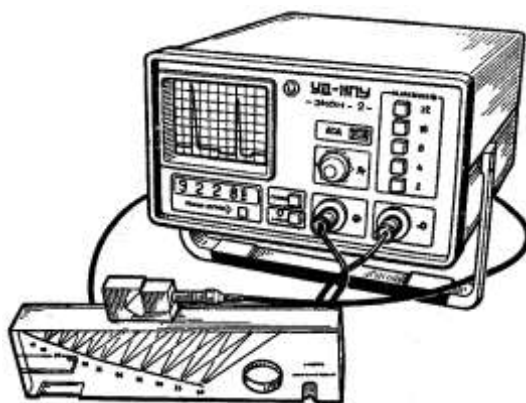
Ультразвуковий дефектоскоп УД-11ПУ для контролю зварних швів
